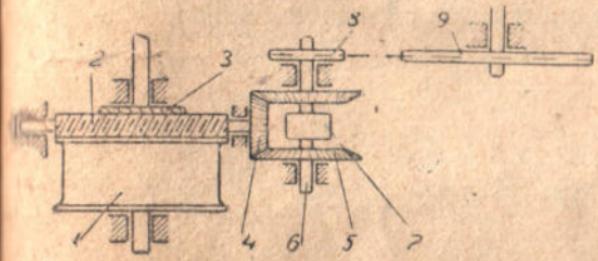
Схема конструкции и управления ведущей лебедкой механизма поворота стрелы.
